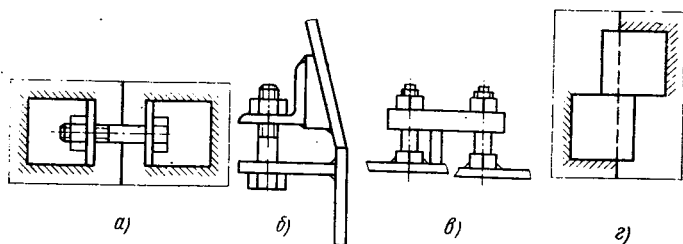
Приспособления для стыковки блоков конденсаторов: а — для стягивания разъемов; б — для стягивания горловины с корпусом; в — для выравнивания кромок листов; г — приварка планок-фиксаторов
